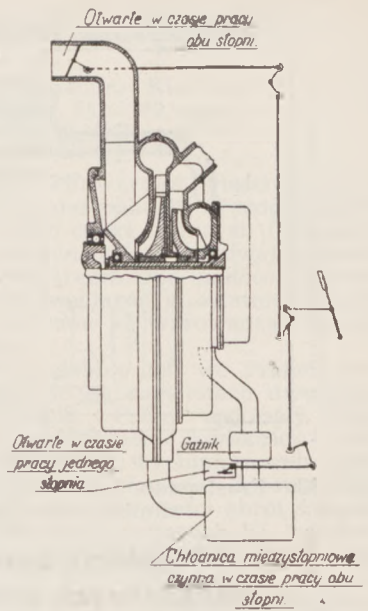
Dwustopniowa sprężarka Farmana dla wysokości około 8500 m. Wirniki na oddzielnych osiach pojedynczo włączalne za pomocą sprzęgieł działających na zasadzie siły odśrodkowej.
